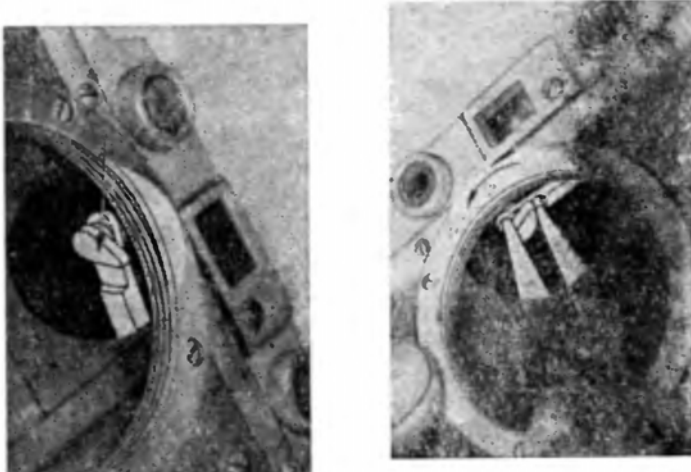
Положение головки скоростей и отвертки при вывинчивании стопорного винта
